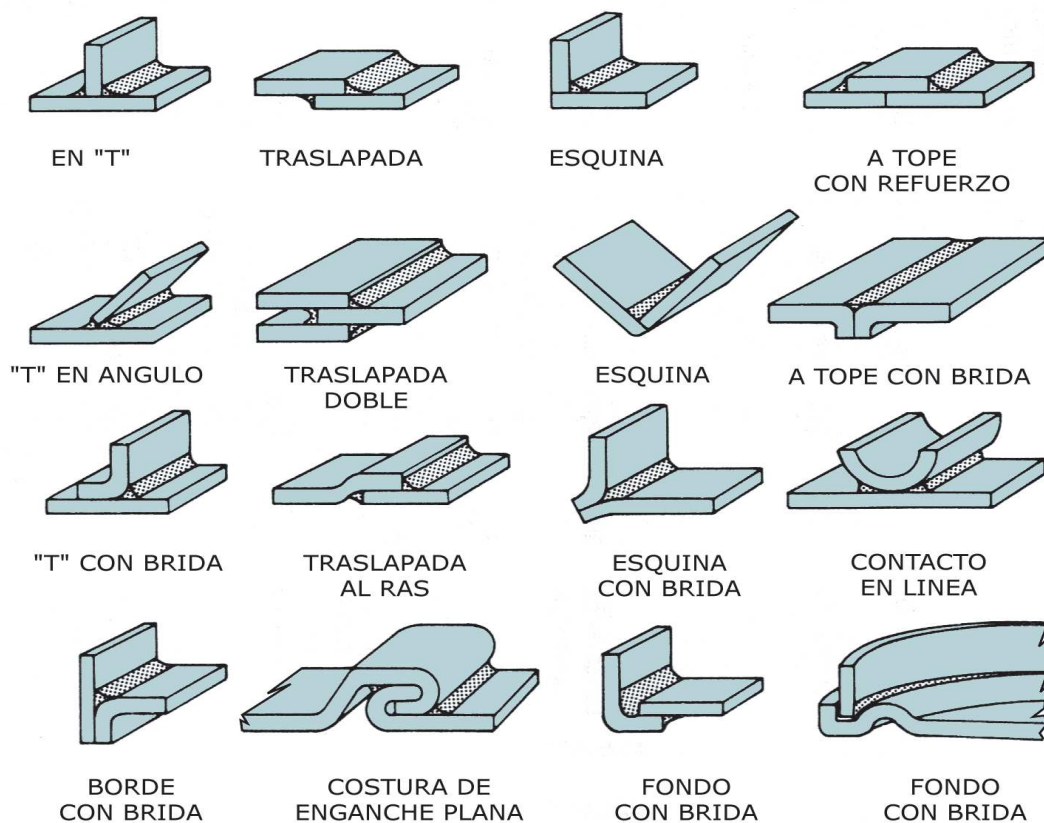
Diseños de uniones habituales en soldadura
